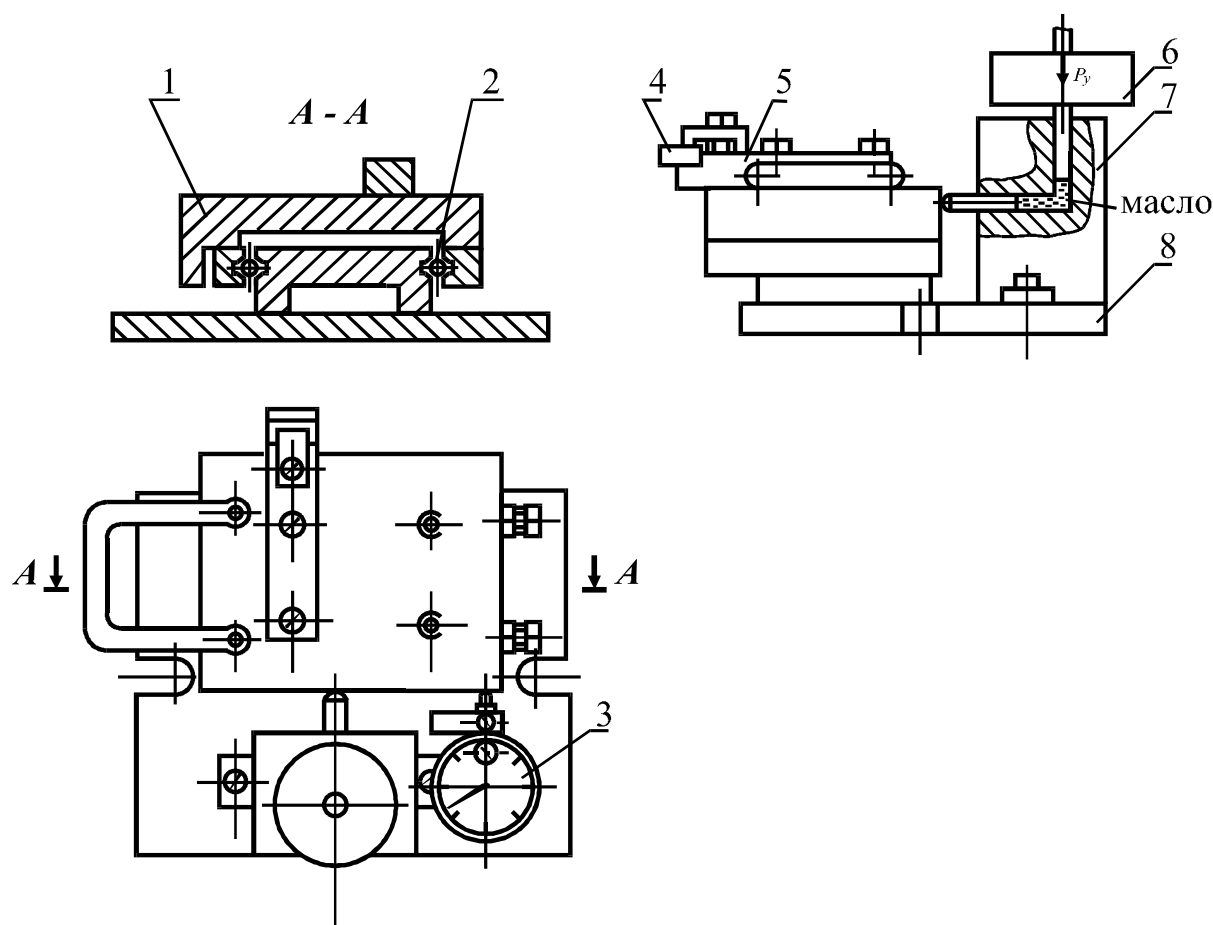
Приспособление для оценки режущей способности алмазных кругов по упругой схеме шлифования:
